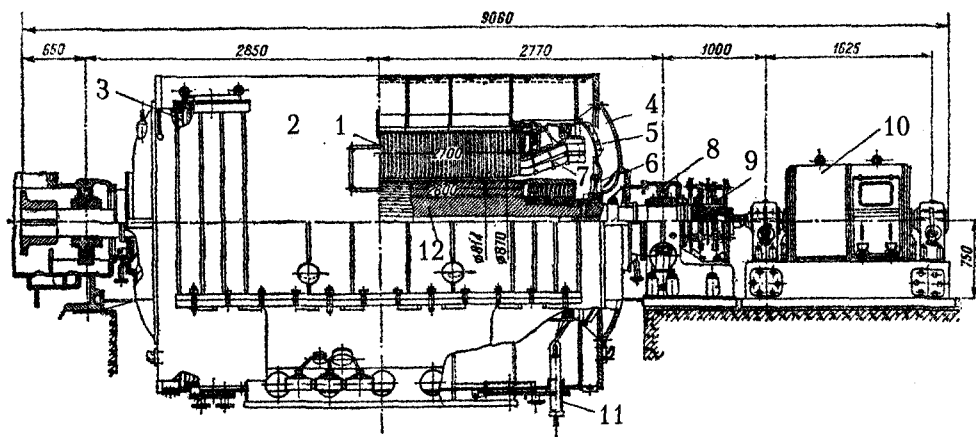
Турбогенератор с косвенным водородным охлаждением, 30 МВт, 10 500 В, 3000 об./мин: 1 — сердечник статора; 2 — сварной корпус статора; 3 — газоохладитель; 4 — наружный щит; 5 — внутренний щит; 6 — осевой вентилятор; 7 — обмотка статора; 8 — подшипниковый стояк с подшипником; 9 — контактные кольца; 10 — возбудитель; 11 — выводы обмотки статора; 12 — ротор
